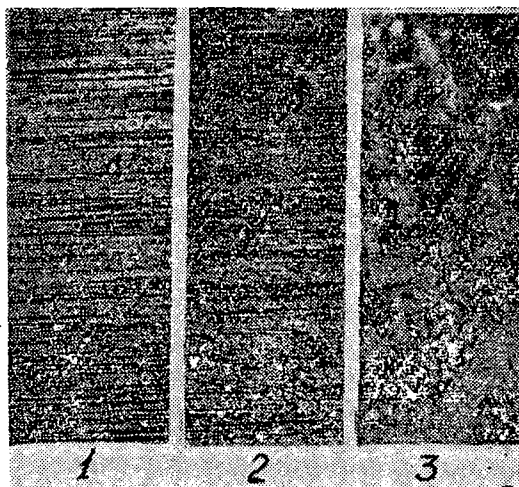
Внешний вид поверхностей деталей подшипников с признаками различных видов изнашивания (увелич. 75 раз).
